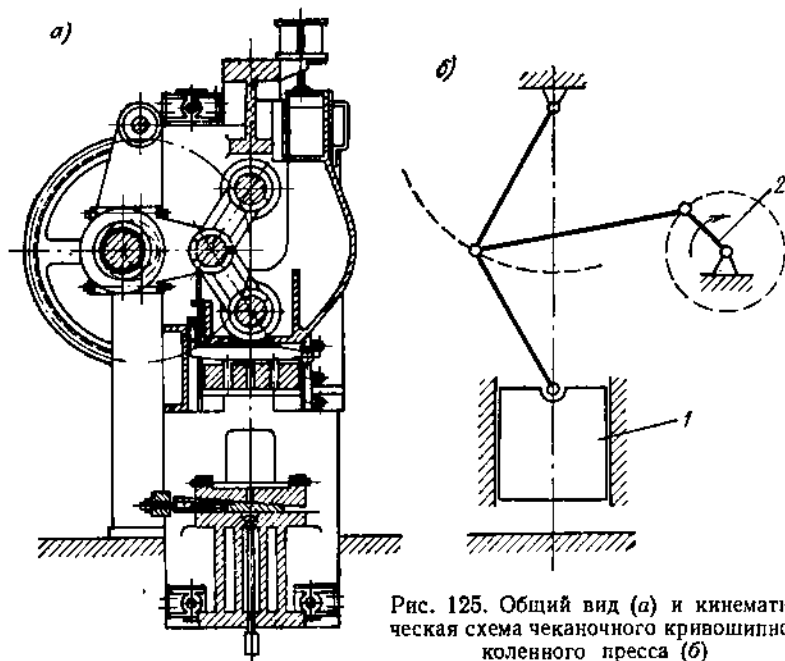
Общий вид (а) и кинематическая схема чеканочного кривошипно-коленного пресса (б)
